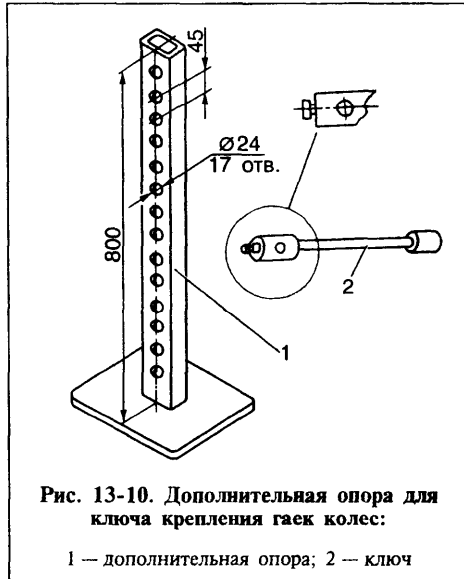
Дополнительная опора для ключа крепления гаек колес:
